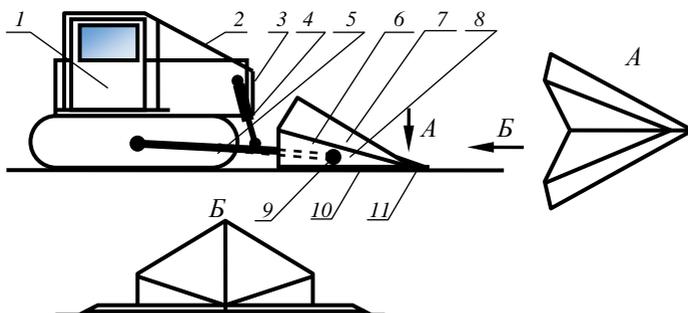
Схема двухотвального кустореза: 1 – трактор базовый; 2 – ограждение; 3 – лист броневой; 4 – гидроцилиндры; 5 – рама толкающая; 6 – рабочий орган; 7 – щиты наклонные; 8 – щиты вертикальные; 9 – шарнир шаровой; 10 – ножи горизонтальные; 11 – клин-колуны
